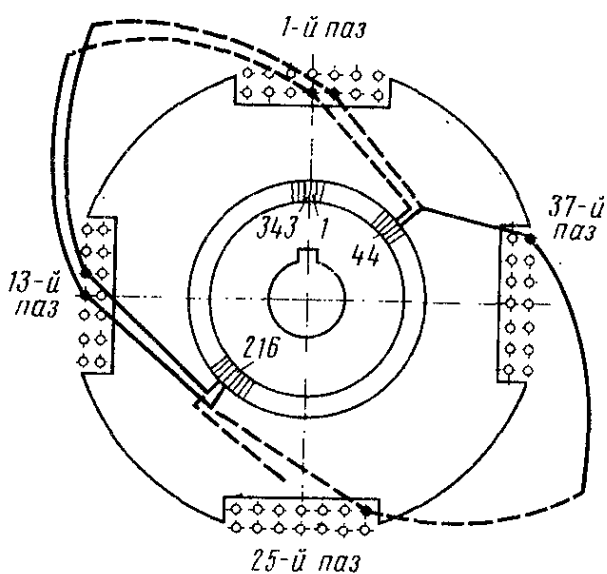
Схема соединения обмотки якоря с коллекторными пластинами электродвигателя НБ-431А
